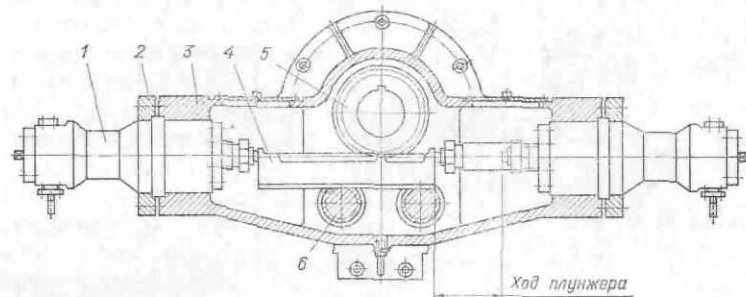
Гидрореечный двухплунжерный привод клапанов и затворов бесконусного загрузочного устройства ВНИИметмаша — ПО «Уралмаш»: 1 — плунжерный гидроцилиндр; 2 — крышка; 3 — корпус; 4 — зубчатая рейка; 5 — шестерня; 6 — ролик поддерживающий
